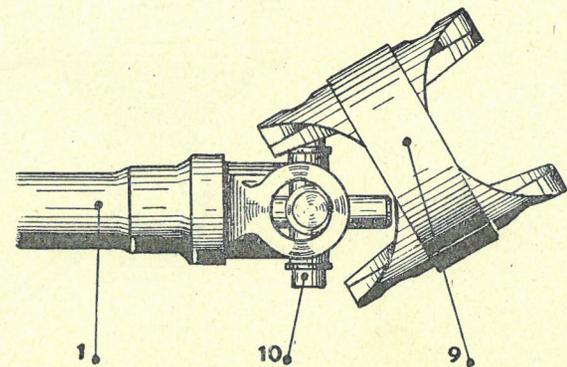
DÉMONTAGE DE LA CUVETTE D'ÉTANCHÉITÉ
